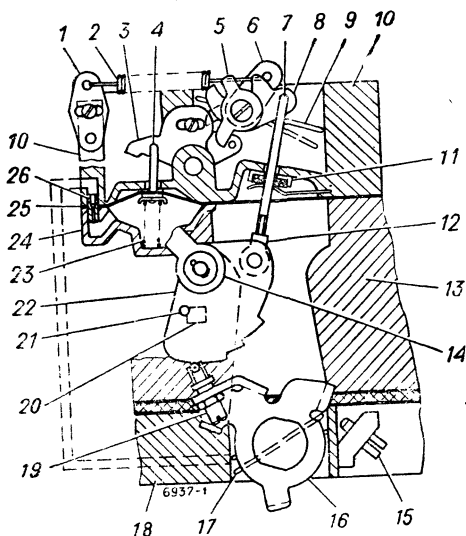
Схема полуавтоматического устройства пуска и прогрева:
